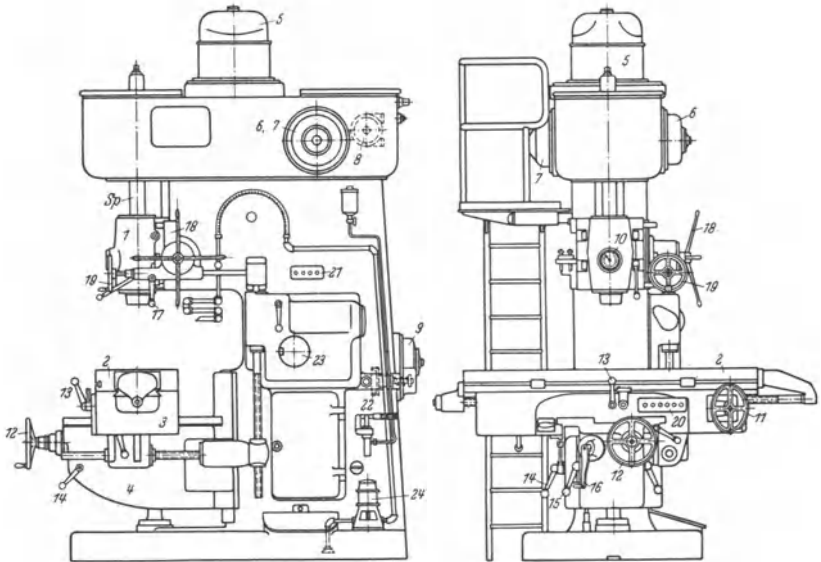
Senkrecht-Fräsmaschine (Fa. Müller & Montag).
